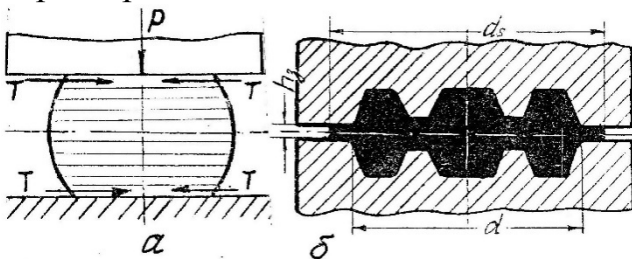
Осадка заготовки між плоскопаралельними бойками (а) і схема гарячого штампування шестерні (б) : Р - сила осадки; Т - сили контактного тертя
